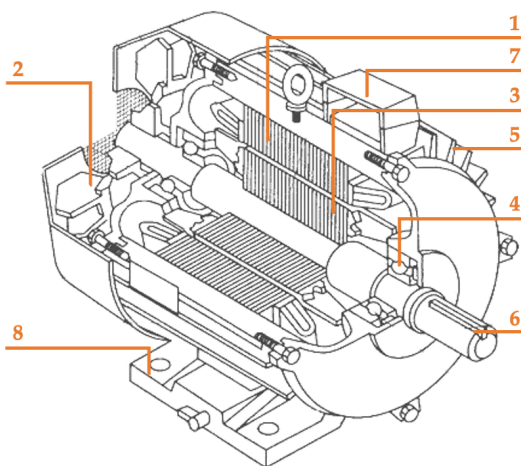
Асинхронный двигатель: 1 – статор; 2 – крыльчатка вентиляции; 3 – короткозамкнутый ротор; 4 – подшипник; 5 – корпус с ребрами охлаждения; 6 – вал; 7 – коробка выводов обмоток статора; 8 – крепления (лапы)
